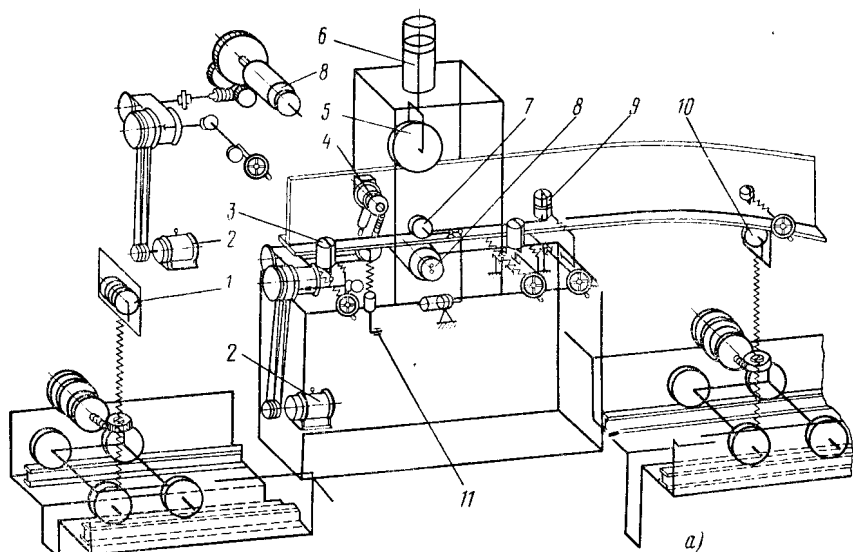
Кінематична схема верстата СТС 2М для складання та зварювання таврових балок
